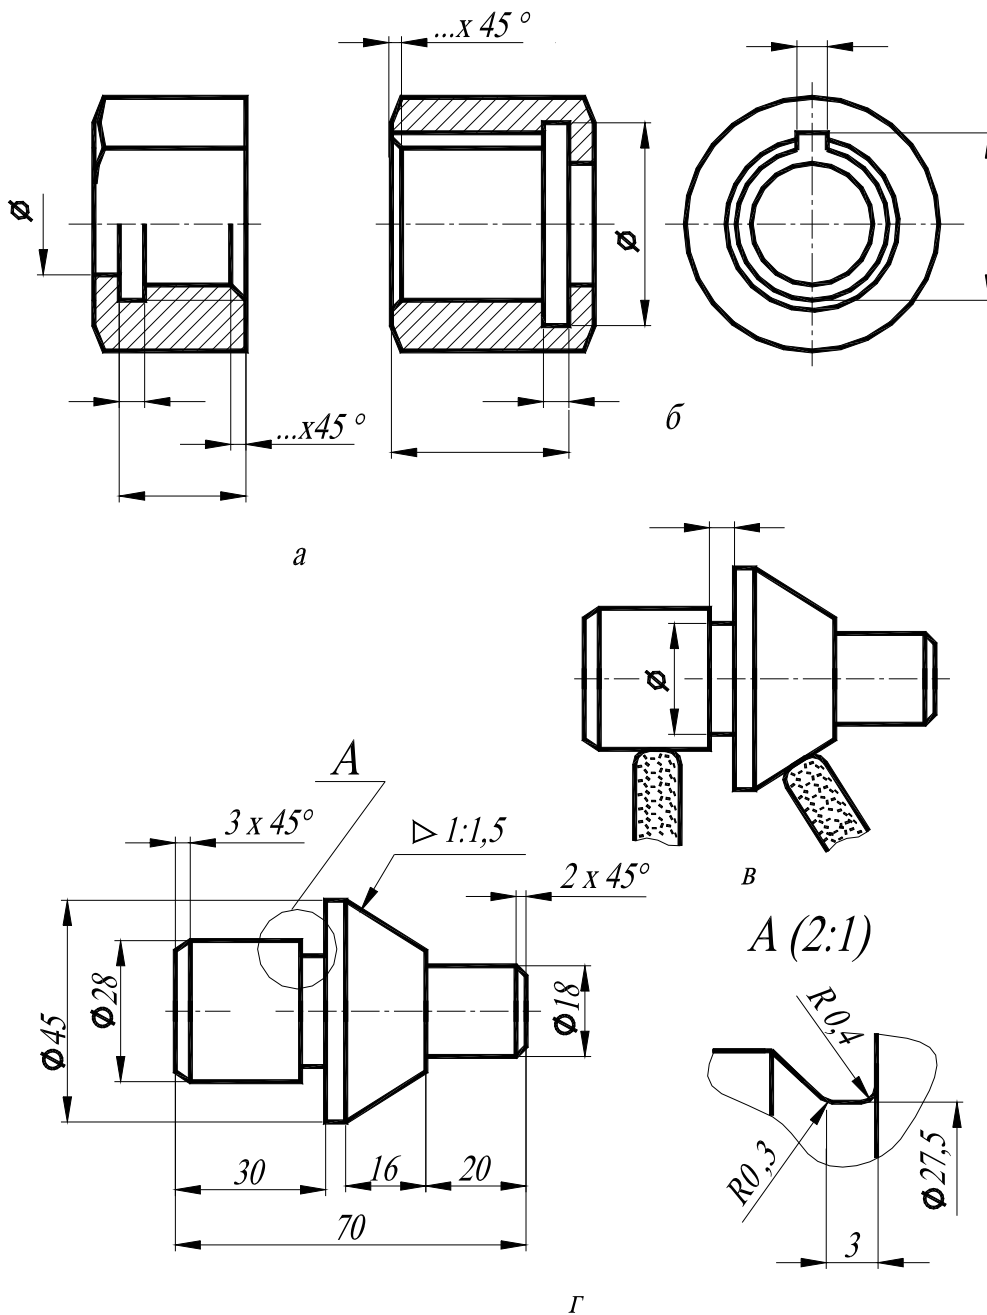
Нанесение размеров с учётом выхода инструмента: а – резьбового резца; б – долбяка; в, г – шлифовального круга
